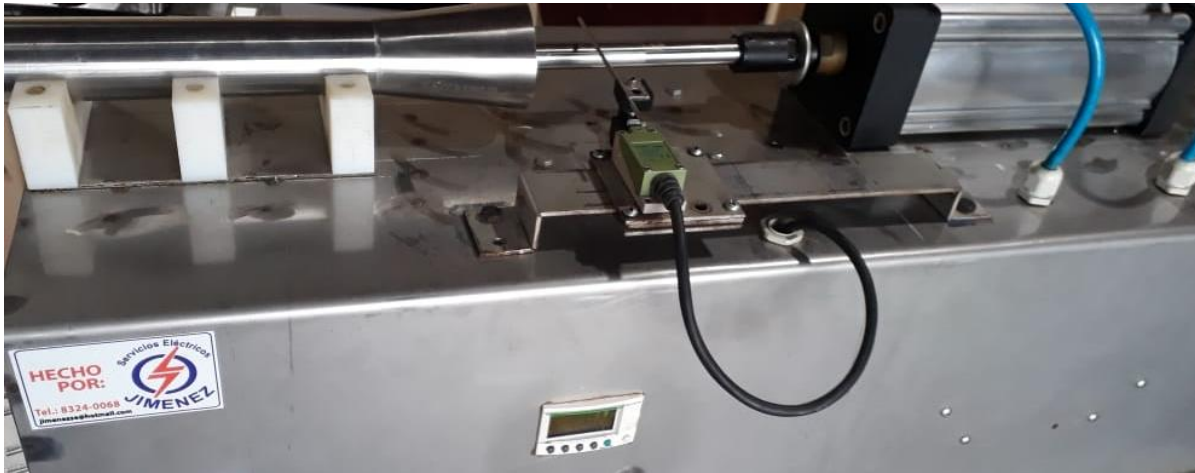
Switch de final de carrera de la máquina actual. Fuente: Elaboración propia.
